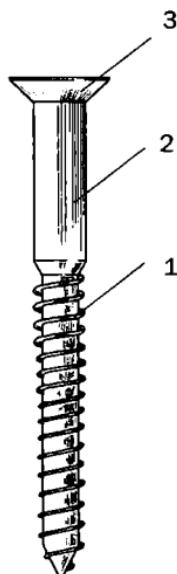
Части стандартного шурупа: 1 — резьба; 2 — тело; 3 — головка
